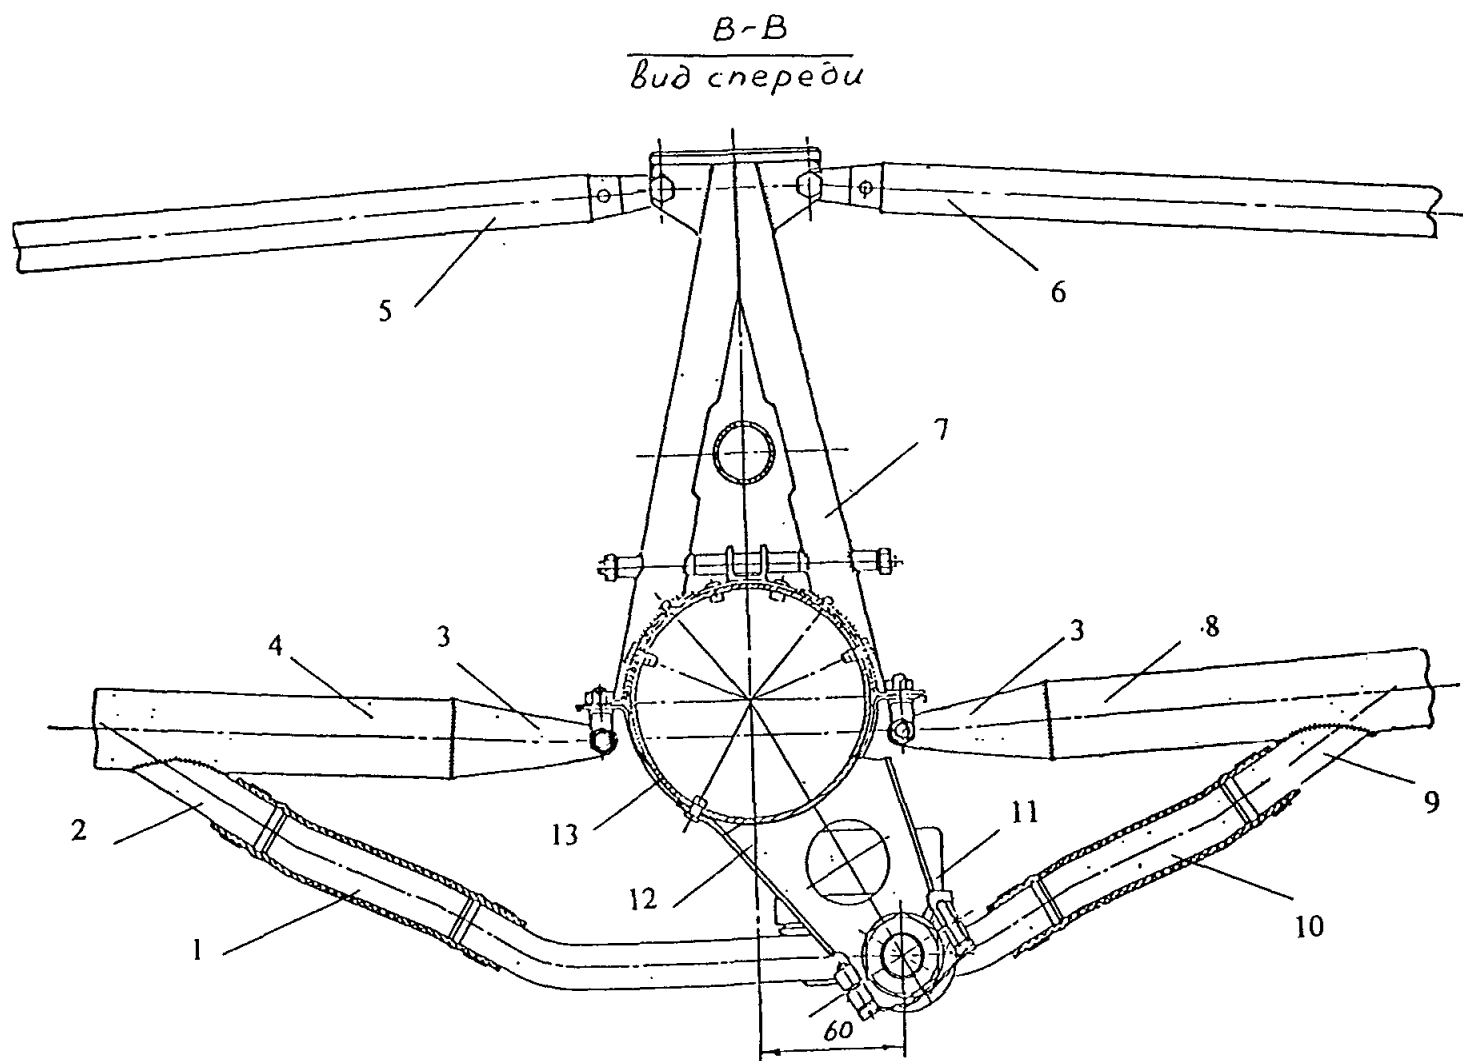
Монтажная схема сельскохозяйственного оборудования (сечение В-В)
